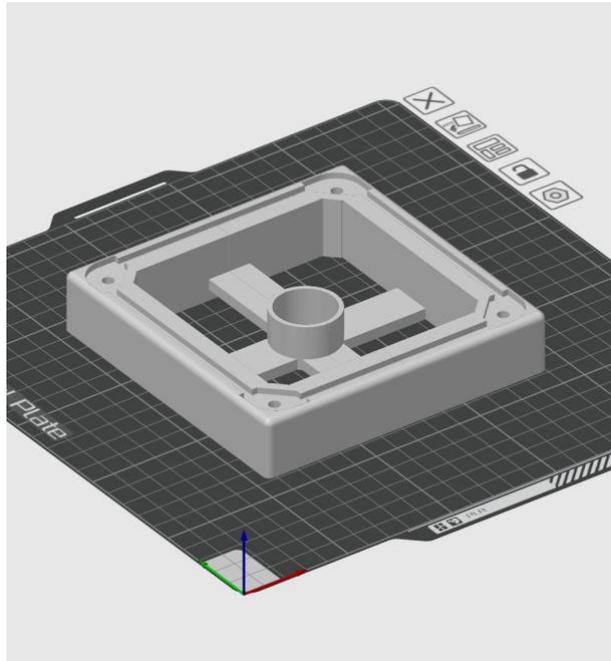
Pieza en vista previa. Fuente: Elaboración propia
